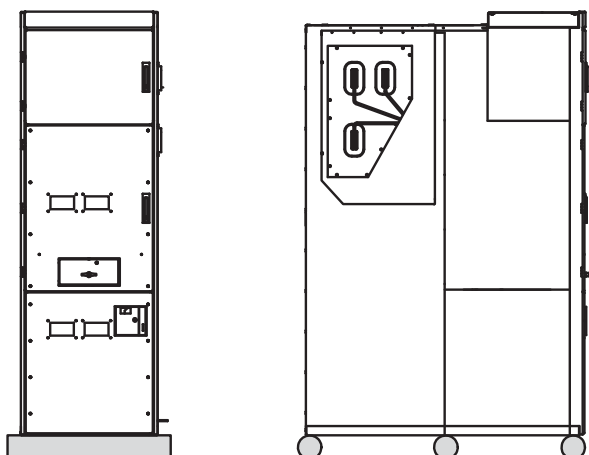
Габаритные размеры базовых ячеек.
